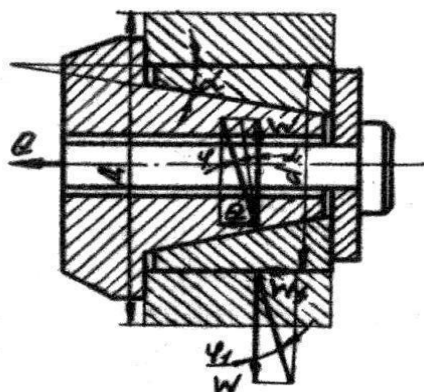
Схема установки заготовки на конічну розрізну втулку
